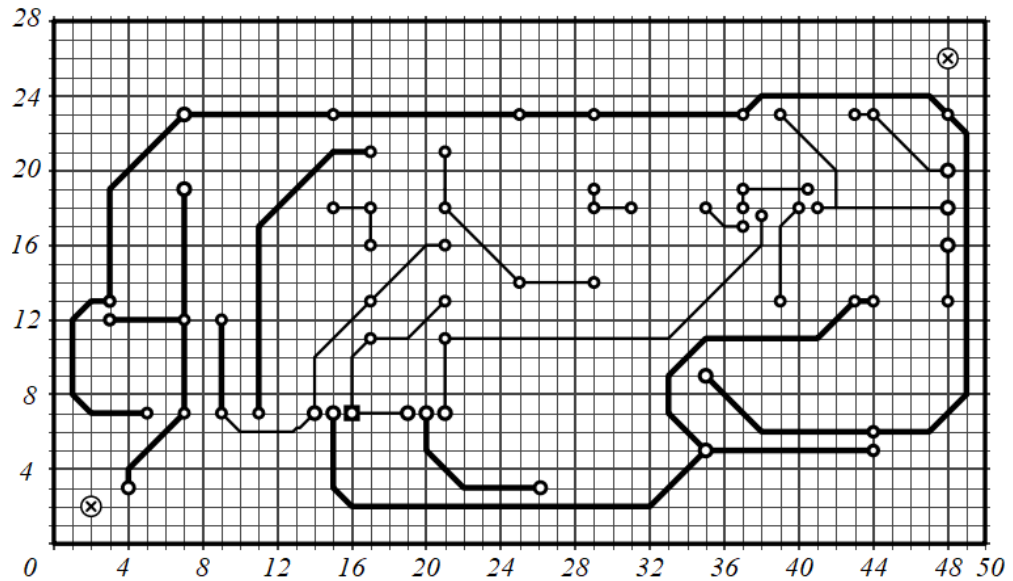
Креслення друкованої плати стабілізатора
